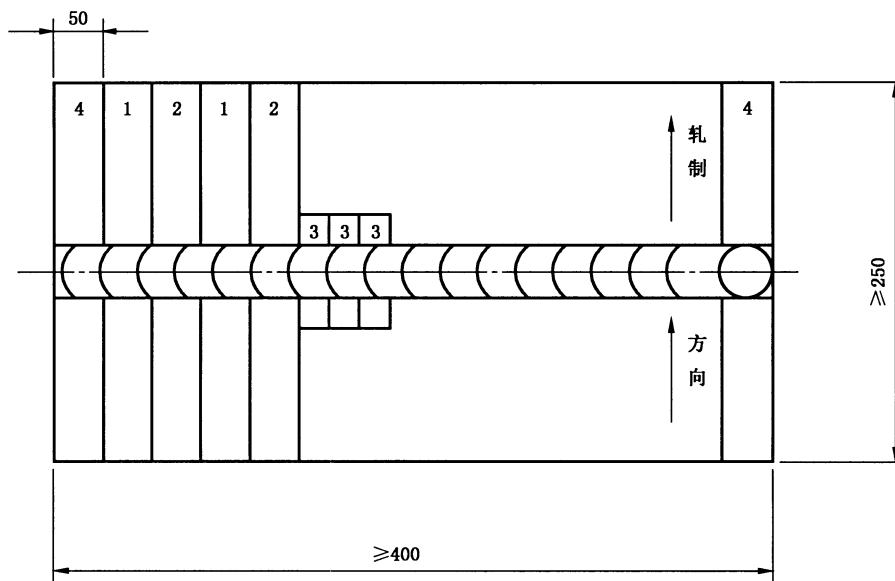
有纵焊缝钢瓶的取样位置示意图
